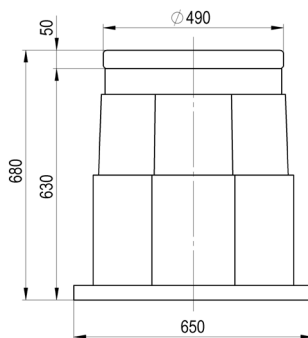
Колодец ККП-2-ССД в сборе, вид сбоку, габаритные размеры
